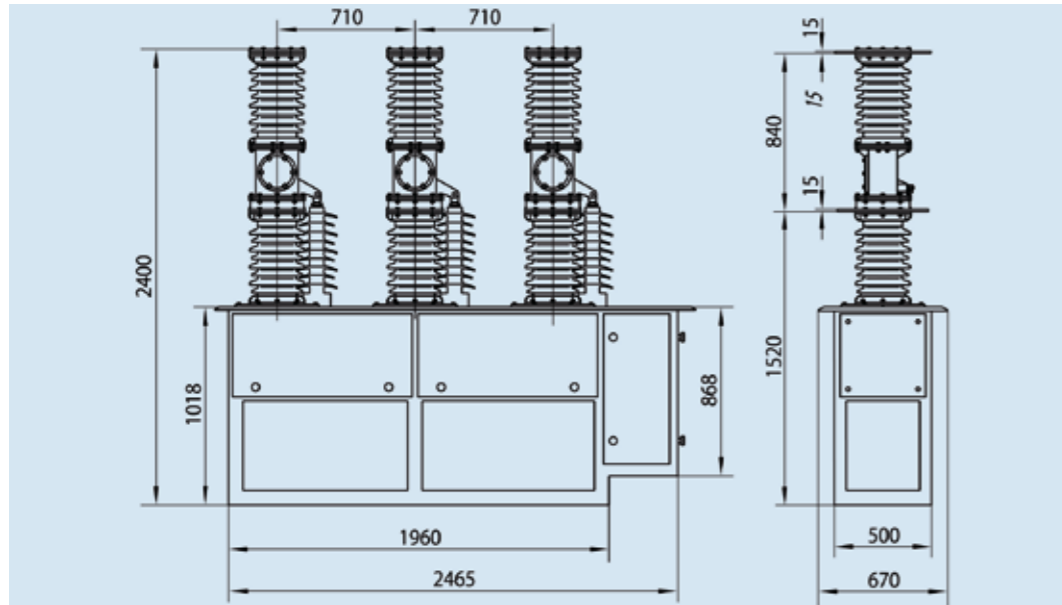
Внешний вид и размеры выключателя ZW7-40.5
